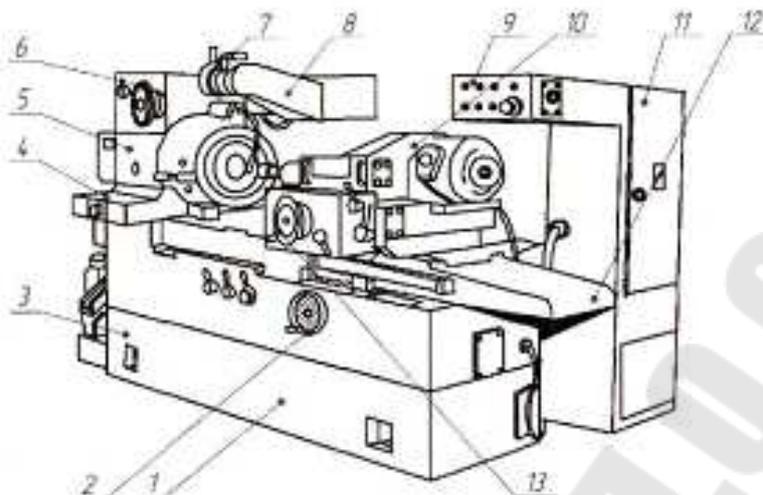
Универсальный внутришлифовальный станок модели 3К228В:
